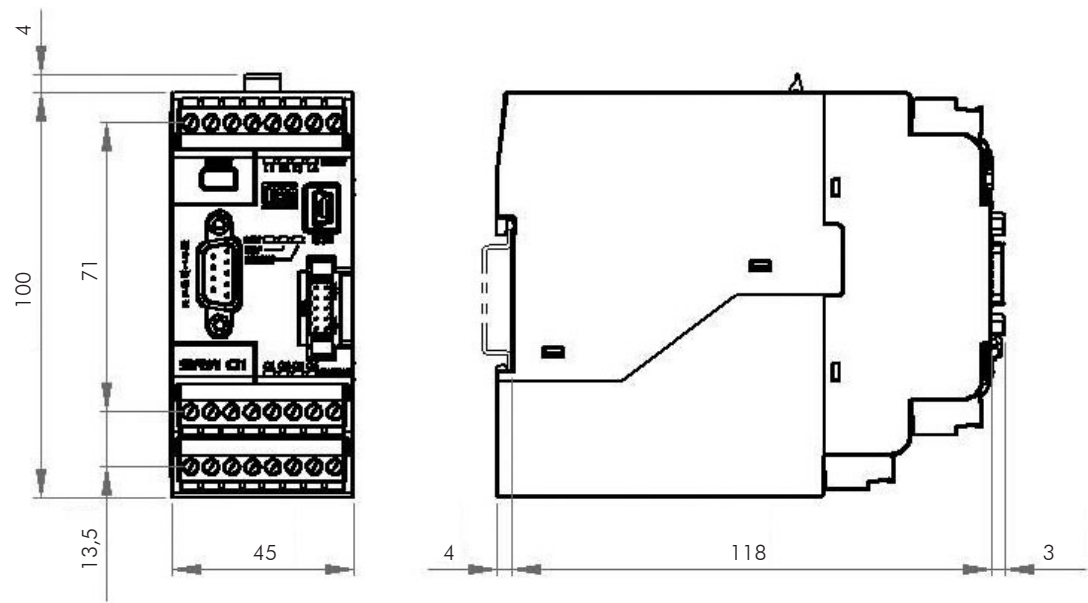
Dimensões da Unidade de Controle – UC (mm)
